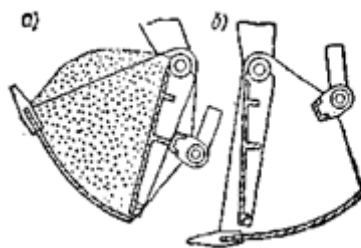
Ковш с поворачивающейся заслонкой [6]
